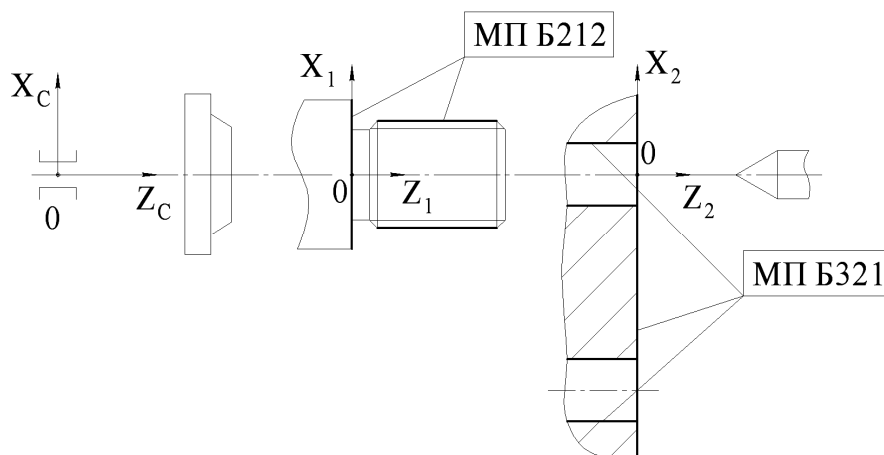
Схема положений поверхностей МП Б212 и МП Б321 в рабочем пространстве токарного станка 16А20Ф3
